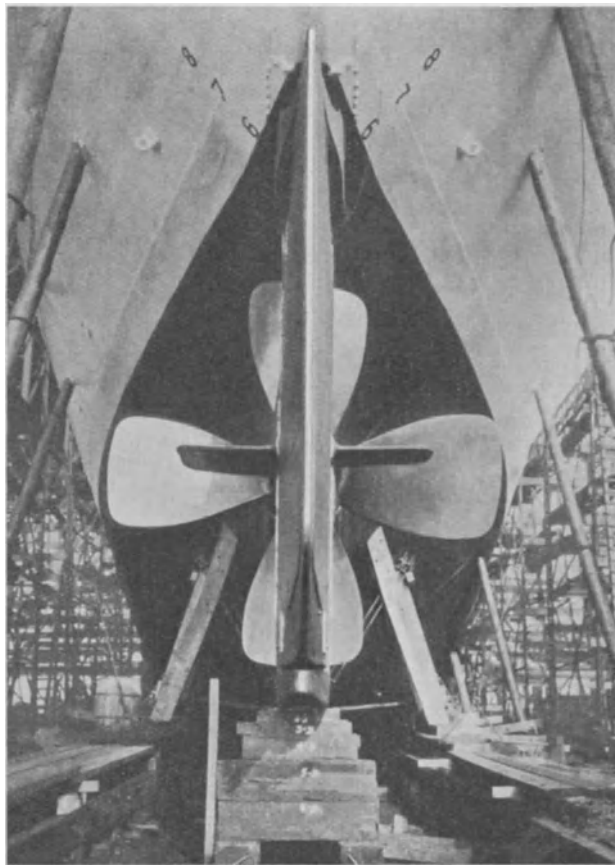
Contraruder kombiniert mit Seitenschaufeln für einen amerikanischen Küstenkreuzer (Hinteransicht).
